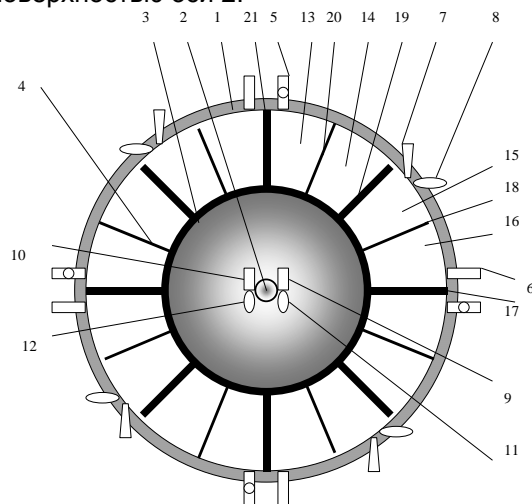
Схема однополостного тора-двигателя со многими лопастно-поршневыми крыльчатками.
